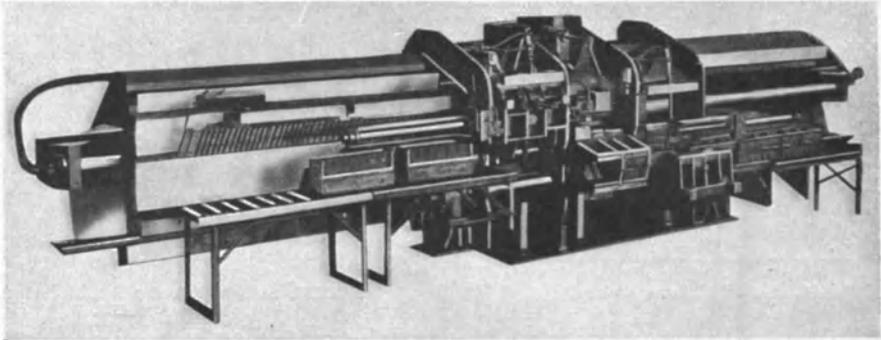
Sonderräummaschine für Zylinderblockbearbeitung.
